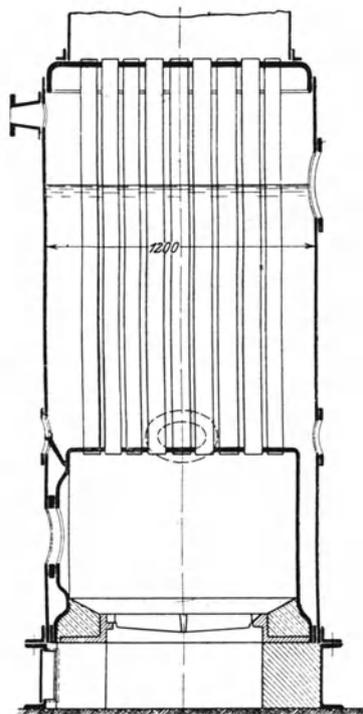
Stehender Kleinkessel mit Rauchröhren. 8 at Dampfdruck. 16 qm Heizfläche.
